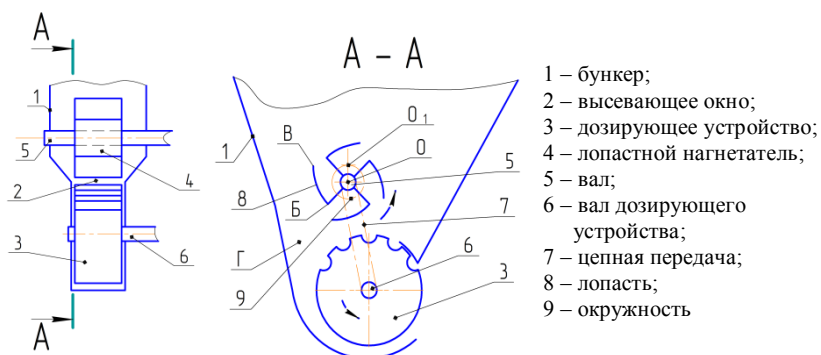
Схема высевашающего аппарата с нагнетателем
